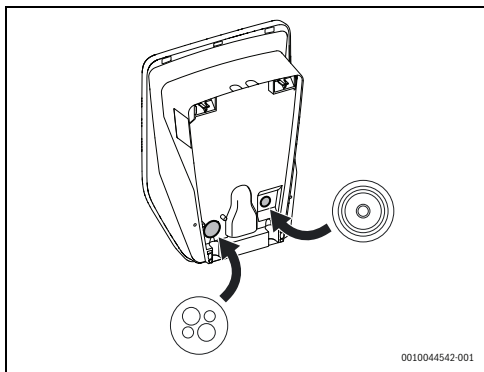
Installazione del passacavo e del pressacavo multiforo (CLIXX)
